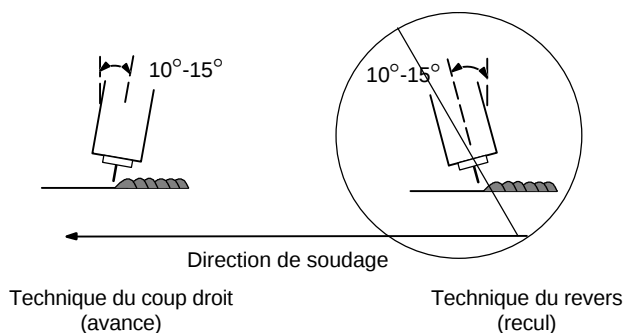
Vue latérale de l'angle du bec du pistolet
